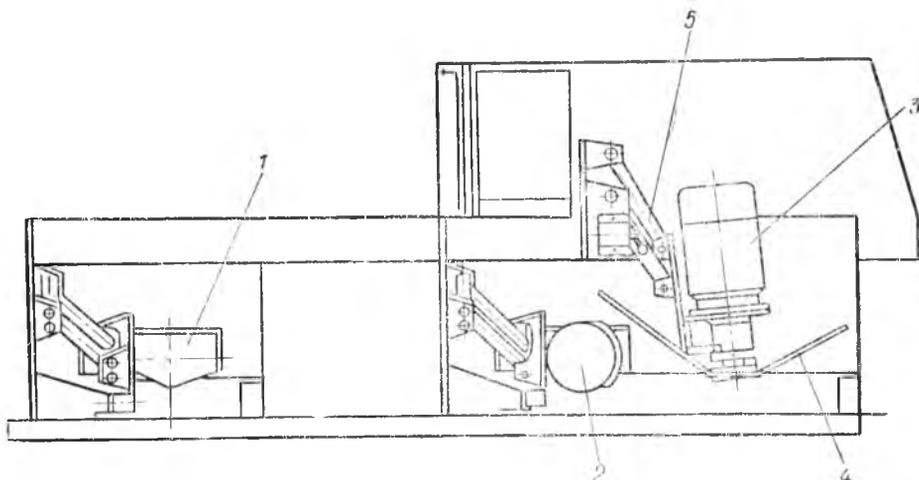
Продольный разрез центрирующего и фрезерующего устройств:
